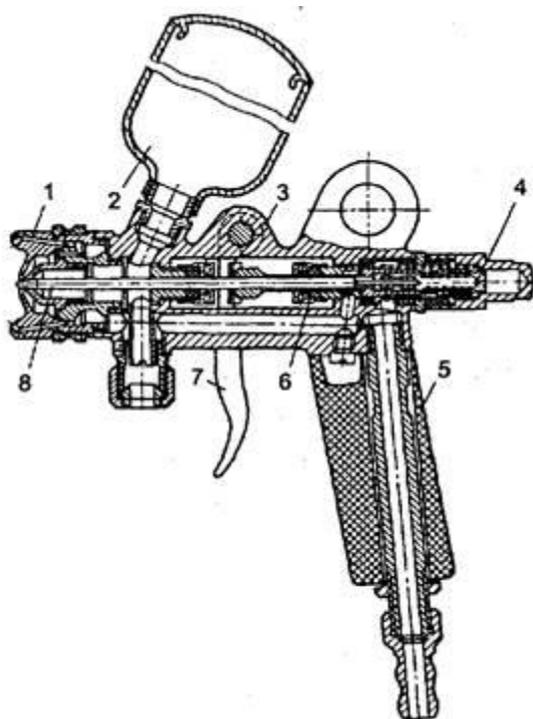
Пневматический пневмораспылитель: 1 — распылительная головка; 2 — бачок для краски; 3 — корпус распылителя; 4 — запорный винт; 5 — ручка; 6 — прокладка; 7 — спусковой крючок; 8 — запорная игла
